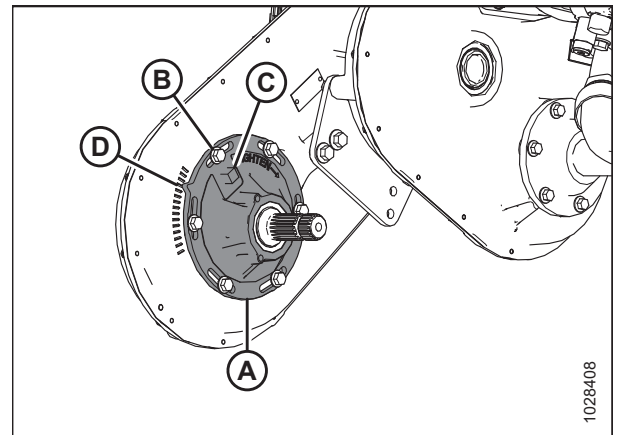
Кришка натягувача ланцюга знижувального редуктора
